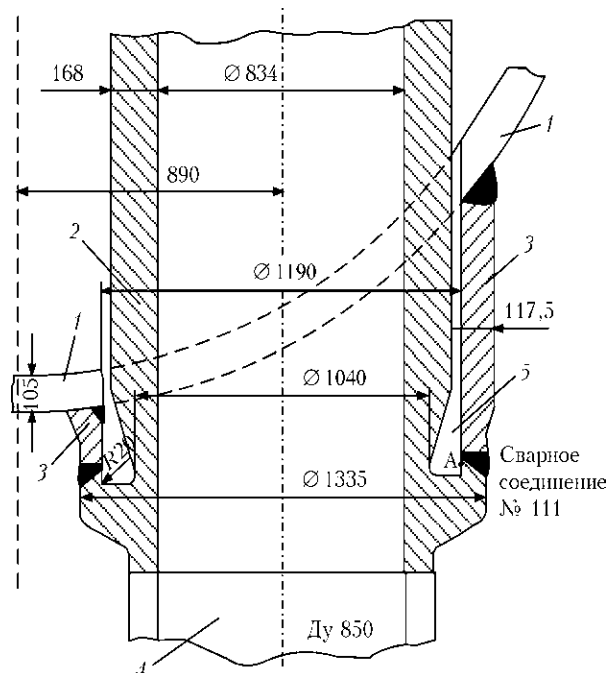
Схема узла соединения коллектора с корпусом парогенератора с помощью патрубка: 1 — корпус парогенератора; 2 — коллектор; 3 — патрубок; 4 — главный циркуляционный трубопровод; 5 — карман
